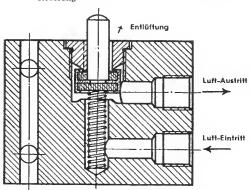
Steuer-Nockenventil, Grundtype 2 für Dreiwegesteuerung
